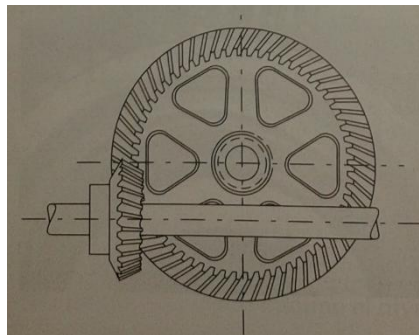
Piñón y corona en un engranaje helicoidal
